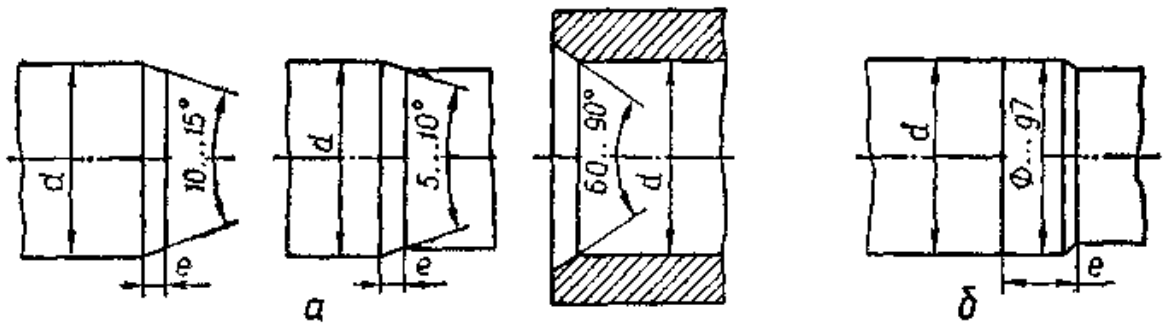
Конструктивні елементи деталей пресового з'єднання
